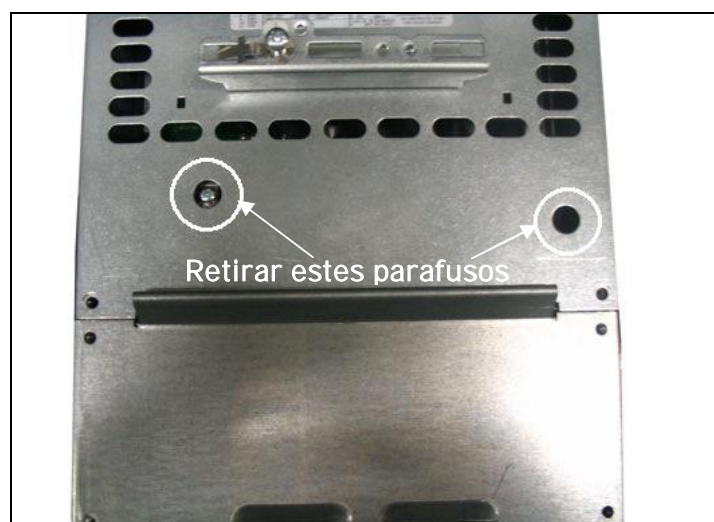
Mudando a classe de proteção EMC, FR6. A tampa do cabo não precisa ser removida.
